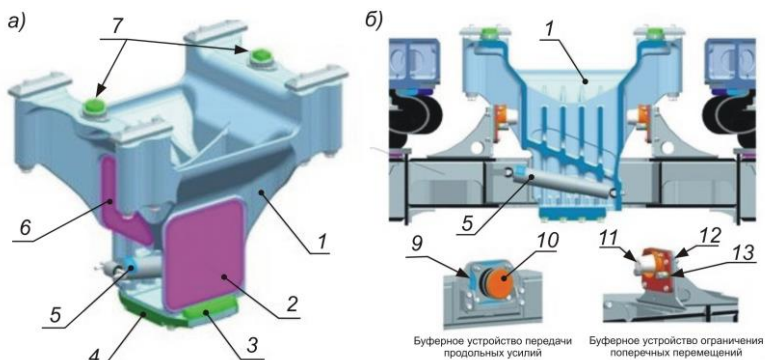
Шкворневой узел тележки электропоезда «Ласточка»: 1 – шкворень; 2, 6 – скользящие; 3 – вставки ограничителя вертикального перемещения; 4 – пластина ограничителя вертикального перемещения; 5 – демпфер гашения поперечных перемещений; 7 – установочные болты; 8 – поперечная балка рамы тележки; 9, 12 – регулировочные вкладыши; 10 – резино-металлический элемент упора; 11 – буфер; 13 – ограничитель поперечных перемещений.
